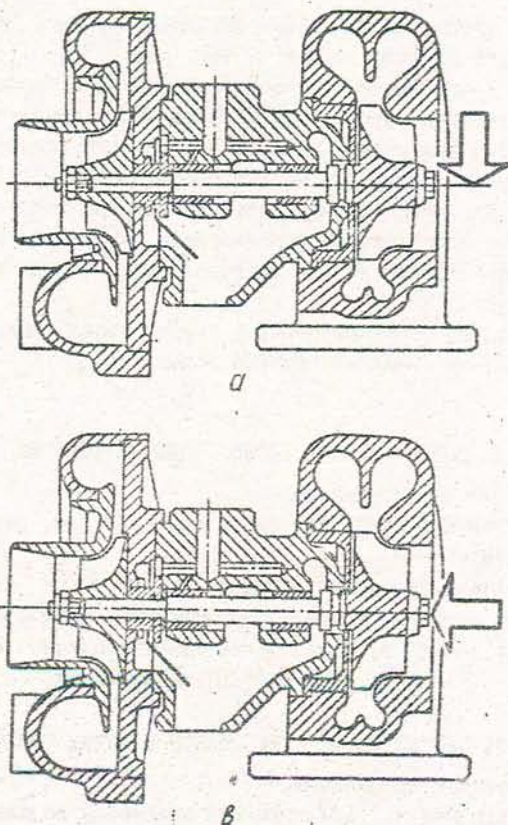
Схема измерения зазора ротора турбокомпрессора:
